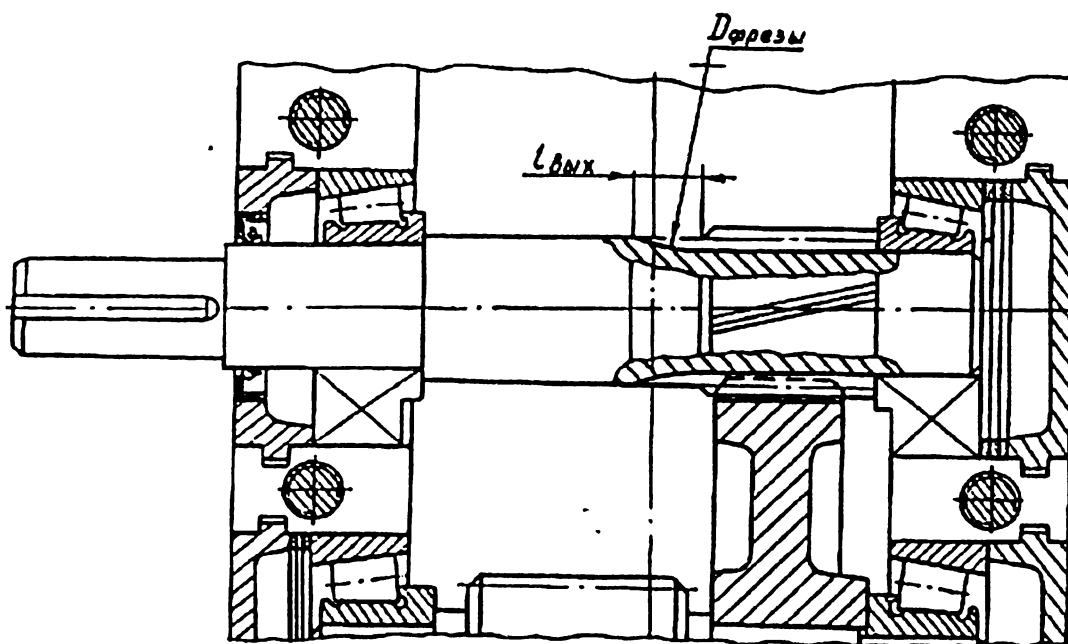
Пример конструкции подшипниковых узлов валов, зафиксированных по схеме «враспор» (крышки подшипников – привертные)
